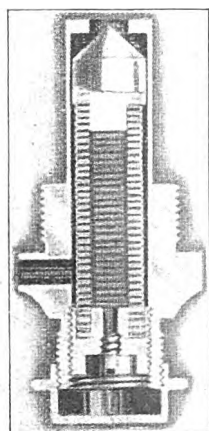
Selbsttätiger Be- und Entlüfter für Heizkörper und Rohrleitungen für Niederdruck- und Hochdruckdampf-Betrieb.
